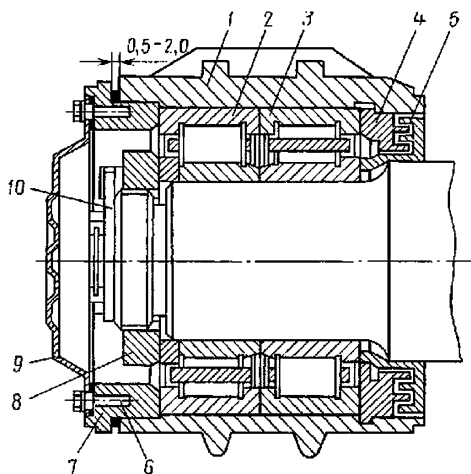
Типовая букса с двумя цилиндрическими роликовыми подшипниками для грузового вагона
